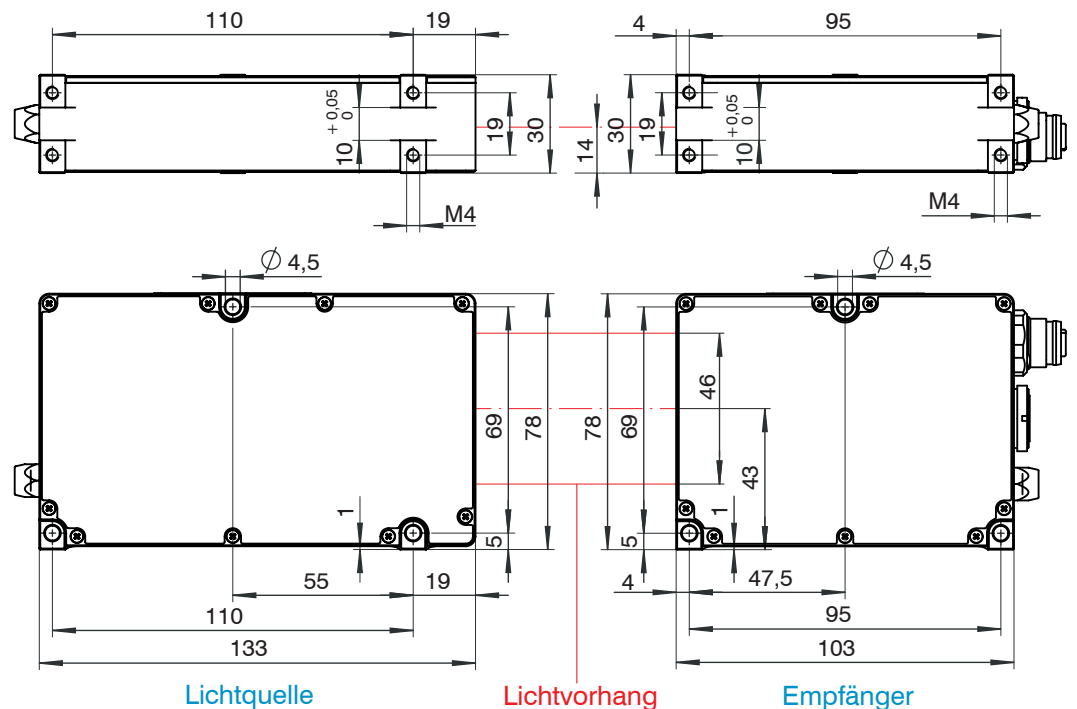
Maßzeichnung optoCONTROL 2520-46, Abmessungen in mm
